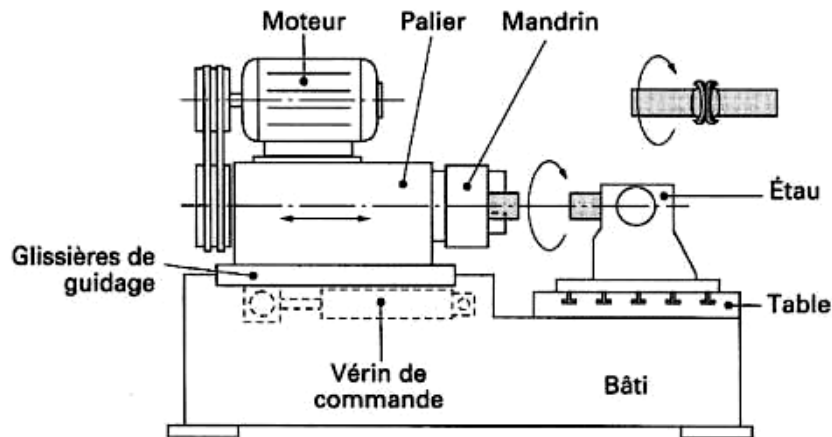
Exemple d'une machine de soudage par friction.
